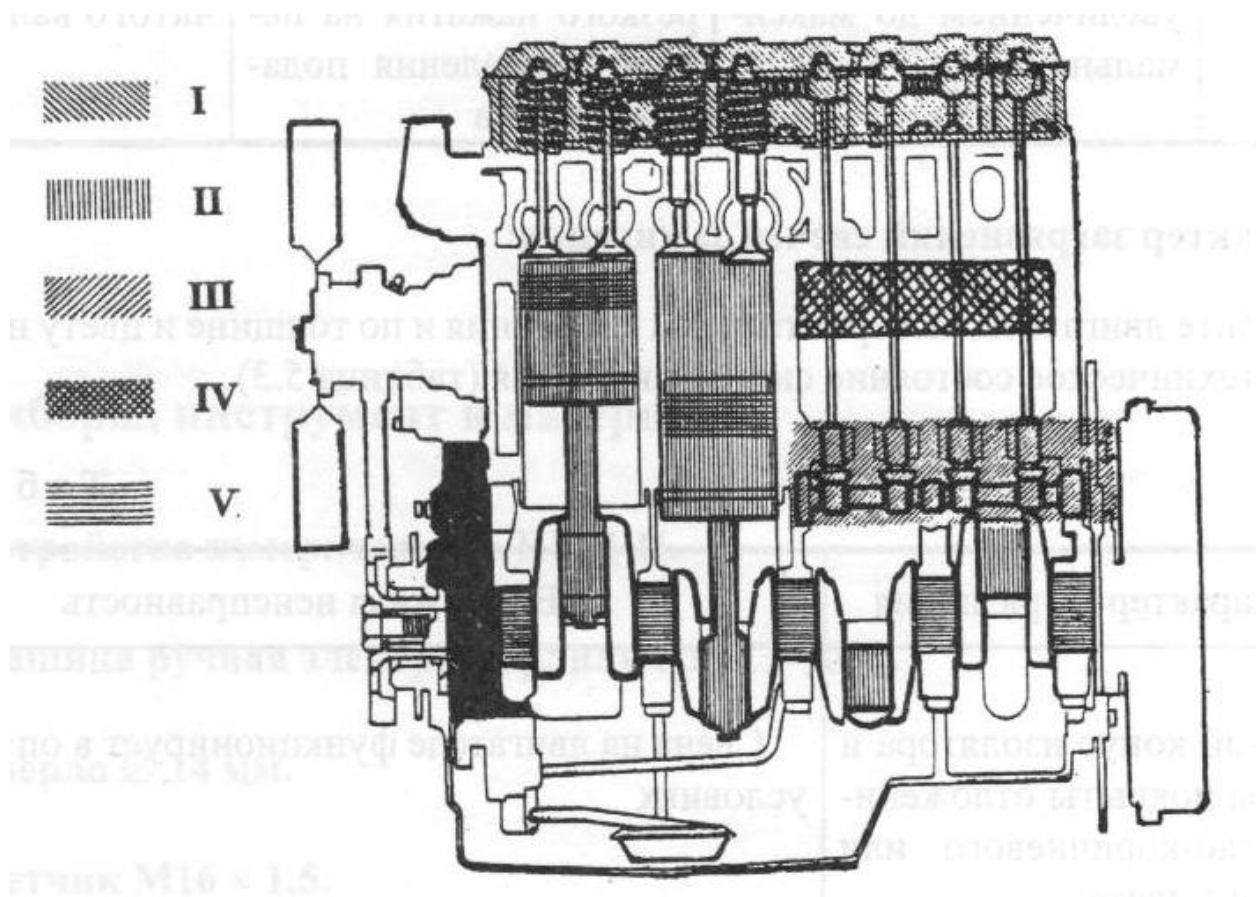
Схема зон прослушивания двигателя: I – зона клапанного механизма; II – зона цилиндропоршневой группы; III – зона нижней мертвой точки (НМТ) поршня; IV – зона верхней мертвой точки (ВМТ); V – зона коренных шеек коленчатого вала
